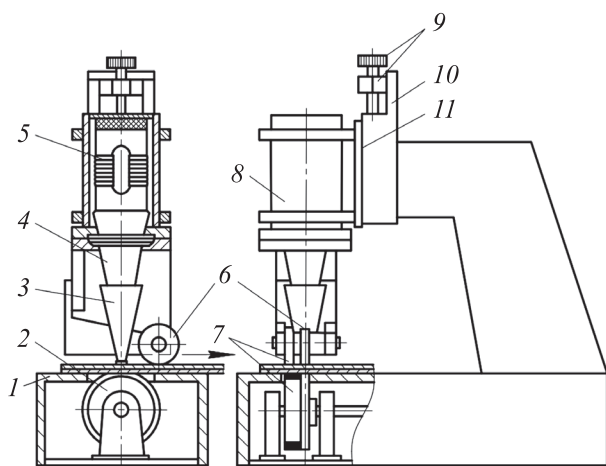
Схема сварочной машины УПШ-12:
